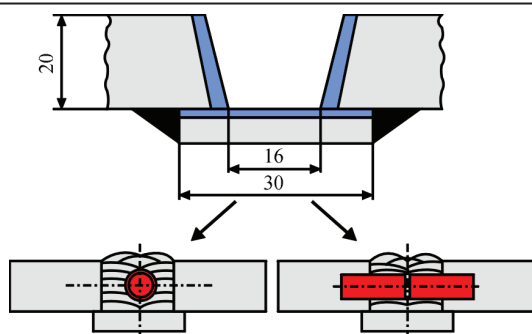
Подготовка кромок и эскизы вырезки из наплавленного металла
